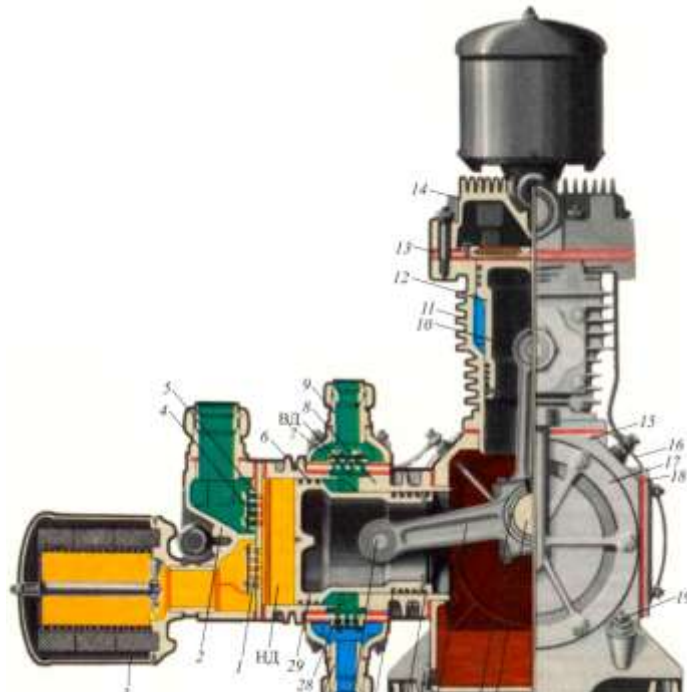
Схема компрессора ВПЗ-4/9:
